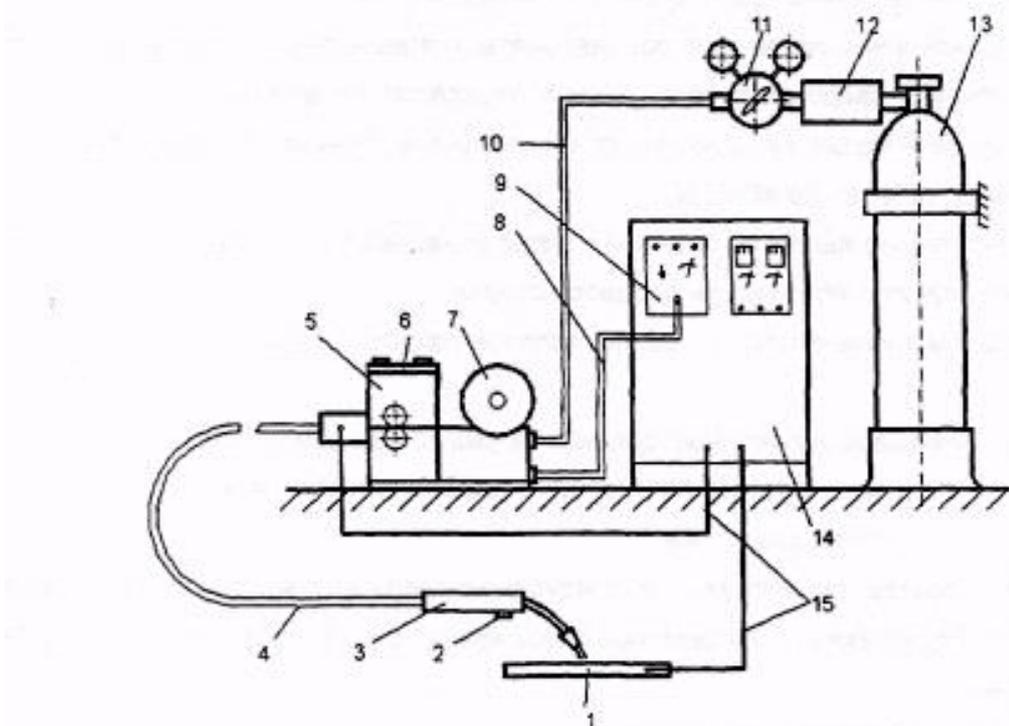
Установка для дуговой механизированной сварки в CO₂: 1 - изделие; 2 - кнопка "Пуск"- "Стоп"; 3 - горелка; 4 - гибкий шланг; 5 - механизм подачи электродной проволоки; 6 - пульт управления; 7 - катушка; 8 - кабель цепей управления; 9 - блок управления по луавтоматом; 10 - шланг для подачи защитного газа; 11 - газовый редуктор; 12 - подогреватель CO₂; 13 - баллон с CO₂; 14 - сварочный выпрямитель.
